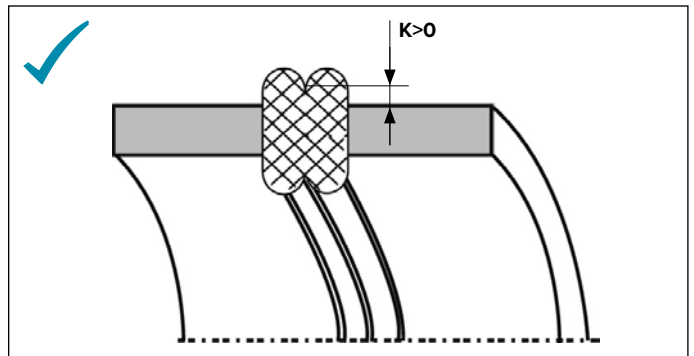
Schnittbild einer guten Schweißnaht
